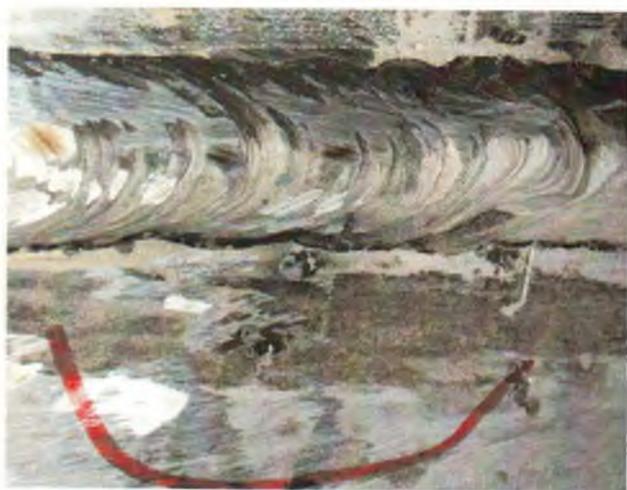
Протяженные подрезы в стыковом сварном соединении плакирующего слоя сосуда. Ширина шва 20...22 мм
